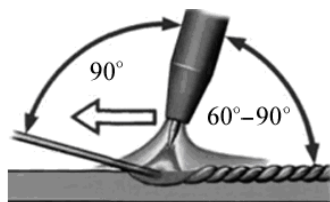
Расположение горелки при аргонно-дуговой сварке
